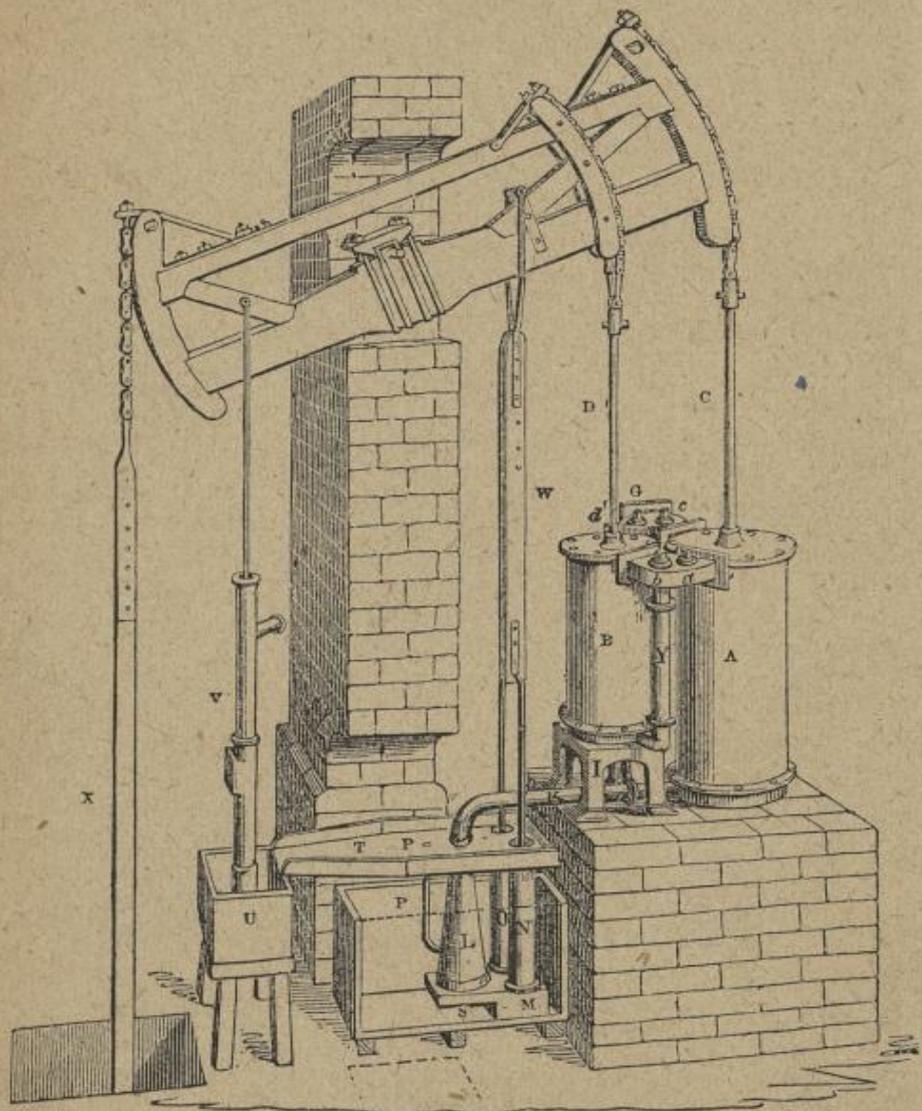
Machine à deux cylindres successifs de Hornblower.
